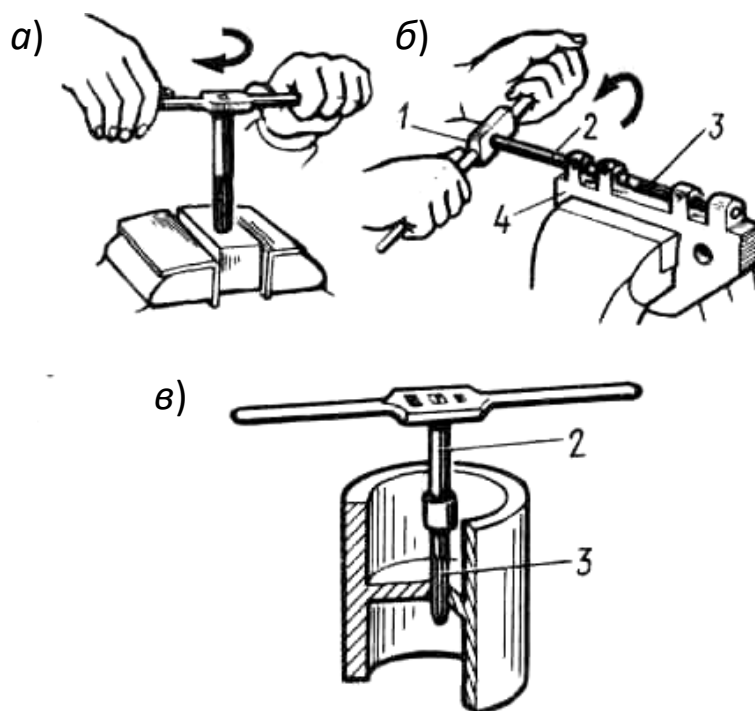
Приемы развертывания отверстий ручными развертками: а) вертикального отверстия; б) горизонтального отверстия; в) в труднообрабатываемом месте; 1 – вороток; 2 – удлинитель; 3 – развертка; 4 – заготовка
